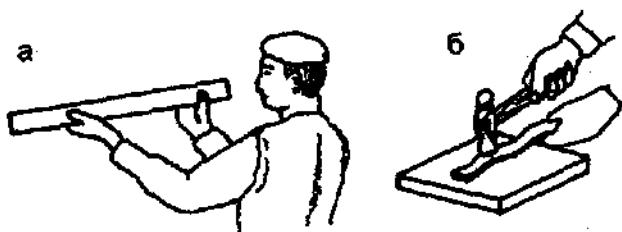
Правка металла: а — проверка на глаз; б — момент правки
